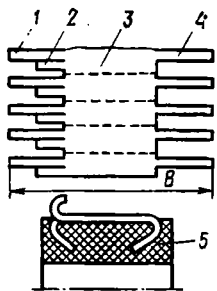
Последовательность операций при изготовлении коллектора из неразделенной заготовки штамповкой полосы
